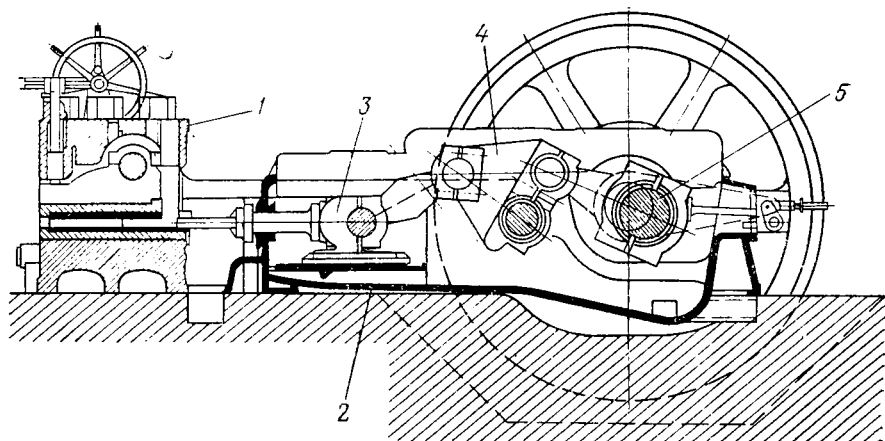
Штемпельный пресс с коленчато-рычажным механизмом:
